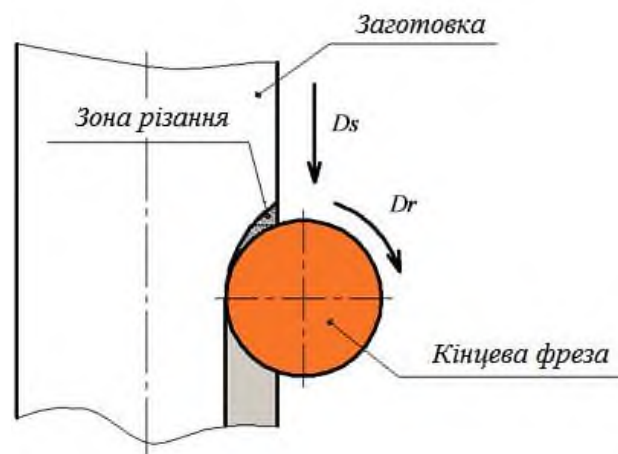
Схема зустрічного фрезерування [24]
